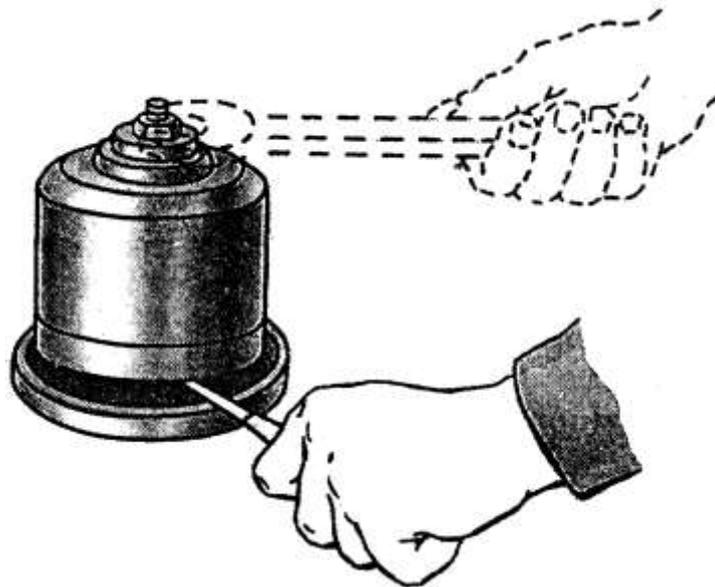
Приём разборки ротора центрифуги с активно-реактивным приводом
